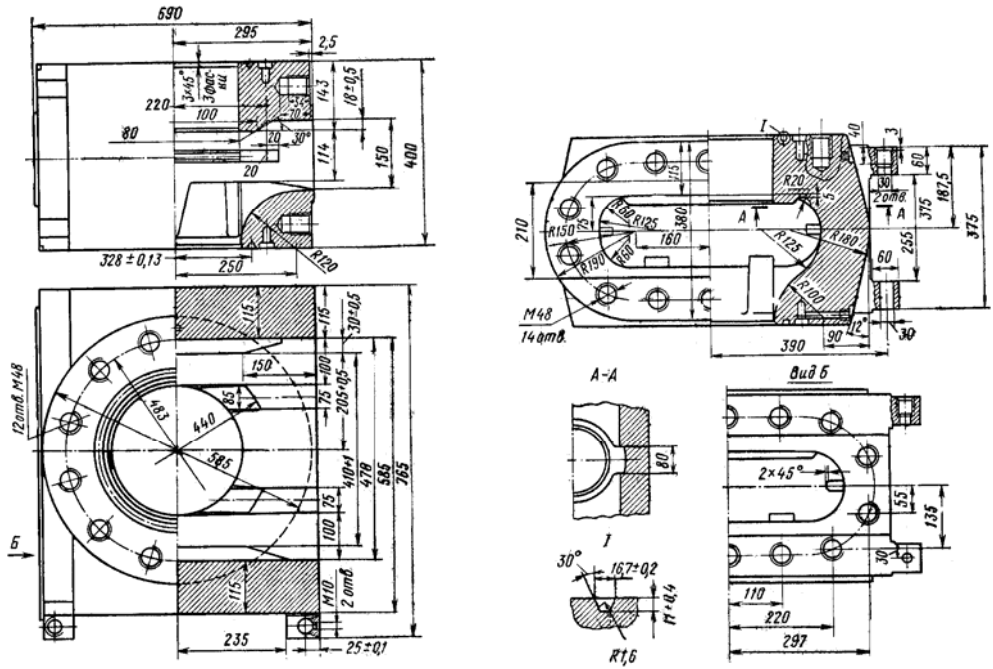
Корпус плащечного преветора ППГ-280×350
